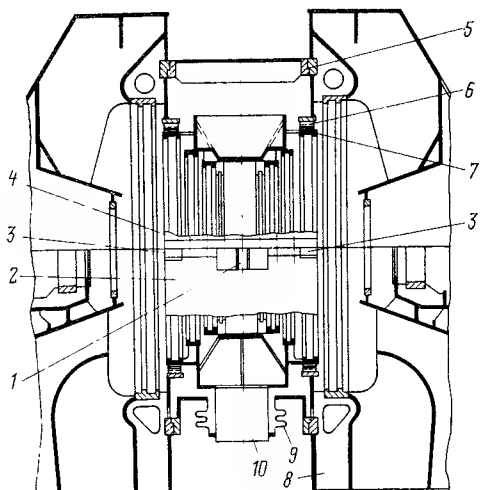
Конструктивная схема двухстенного корпуса ЦНД:
